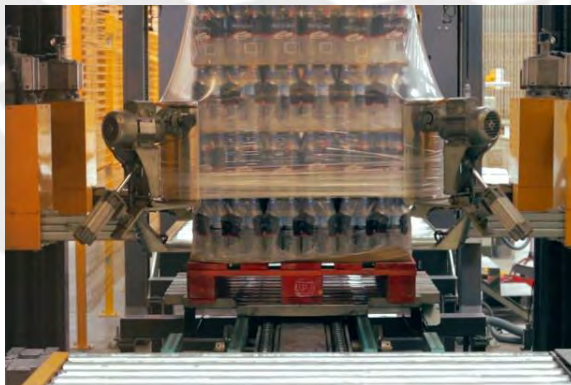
Máquina de embalaje con "Stretch Hood". Fuente: [21].
